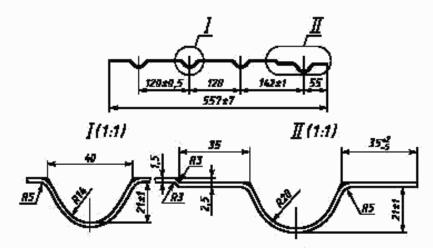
Профиль 557-21-1,5, ГЛ4-238
